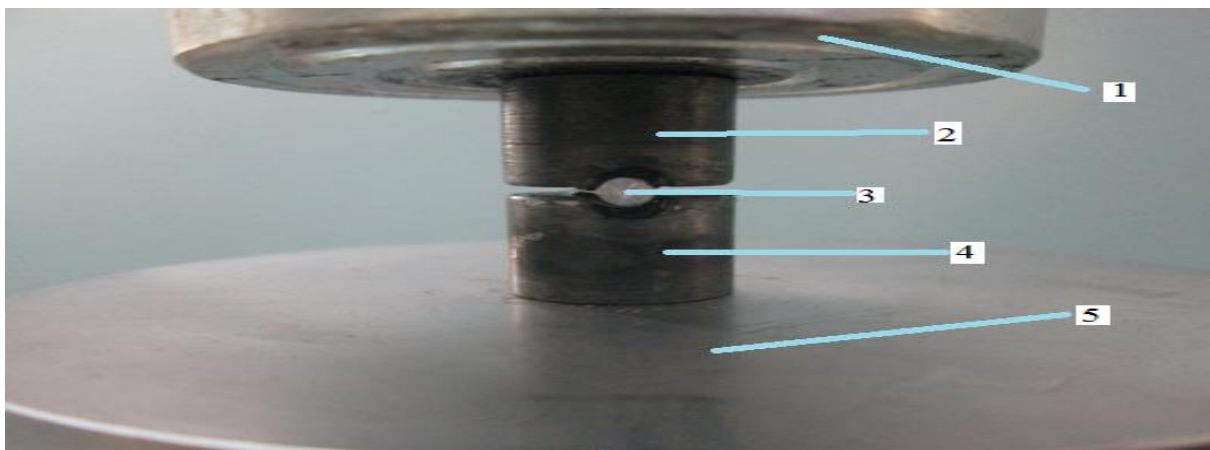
Процесс деформации заготовки: 1 – плунжер прессы; 2 – верхняя половина формы; 3 – алюминиевая заготовка; 4 – нижняя половина формы; 5 – столик прессы
